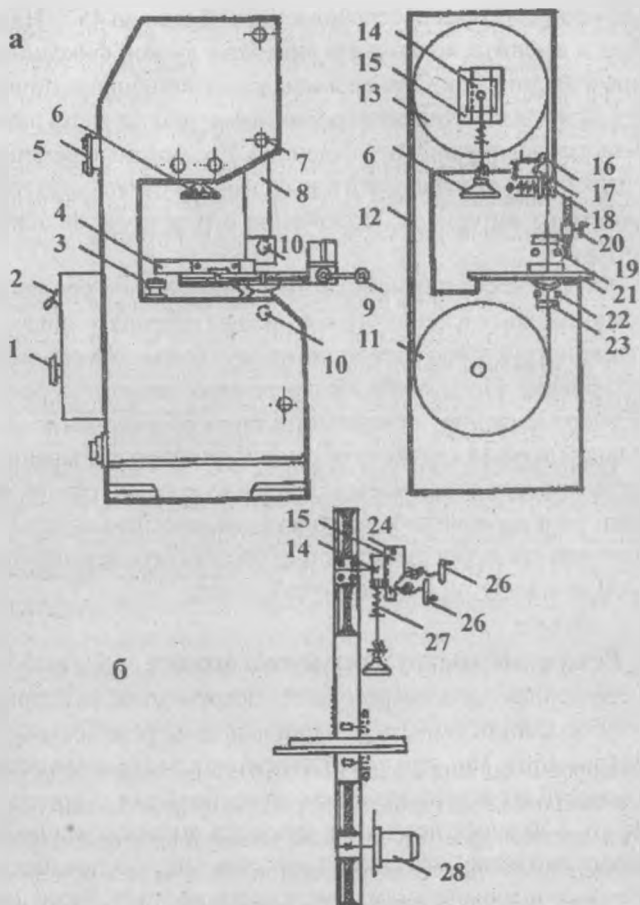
Столярный ленточнопильный станок ЛС40-1:
